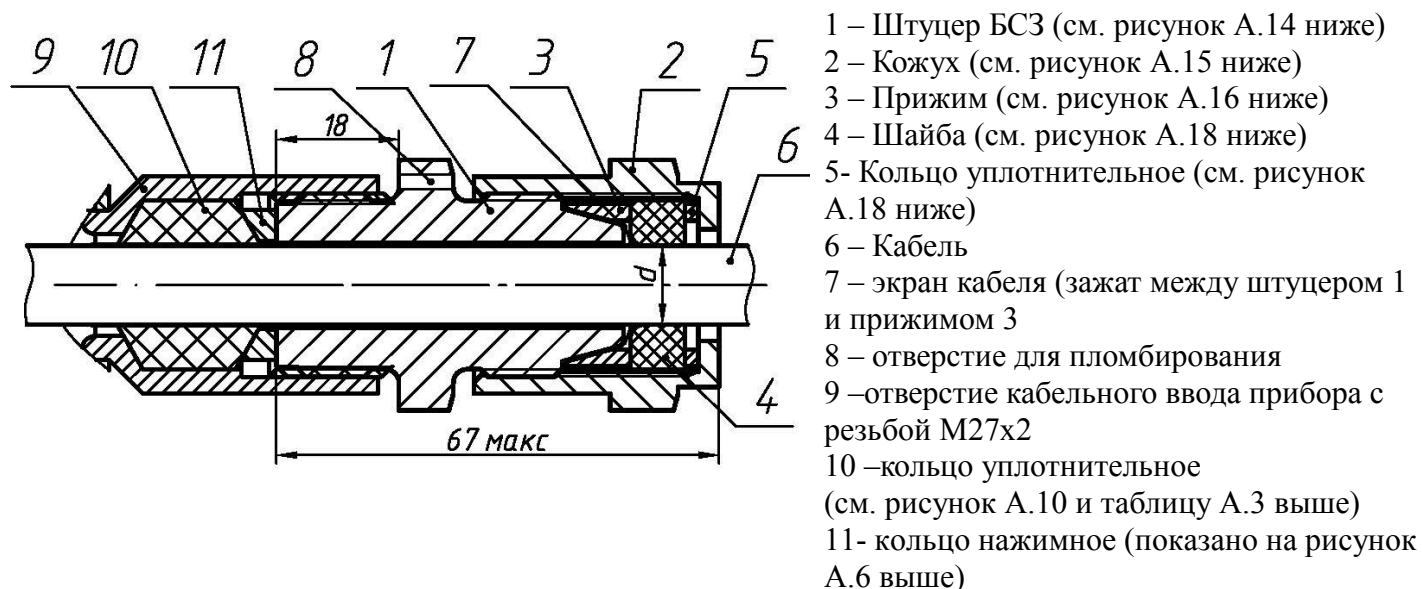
Штуцер БСЗ-14 и БСЗ-18 в сборе
